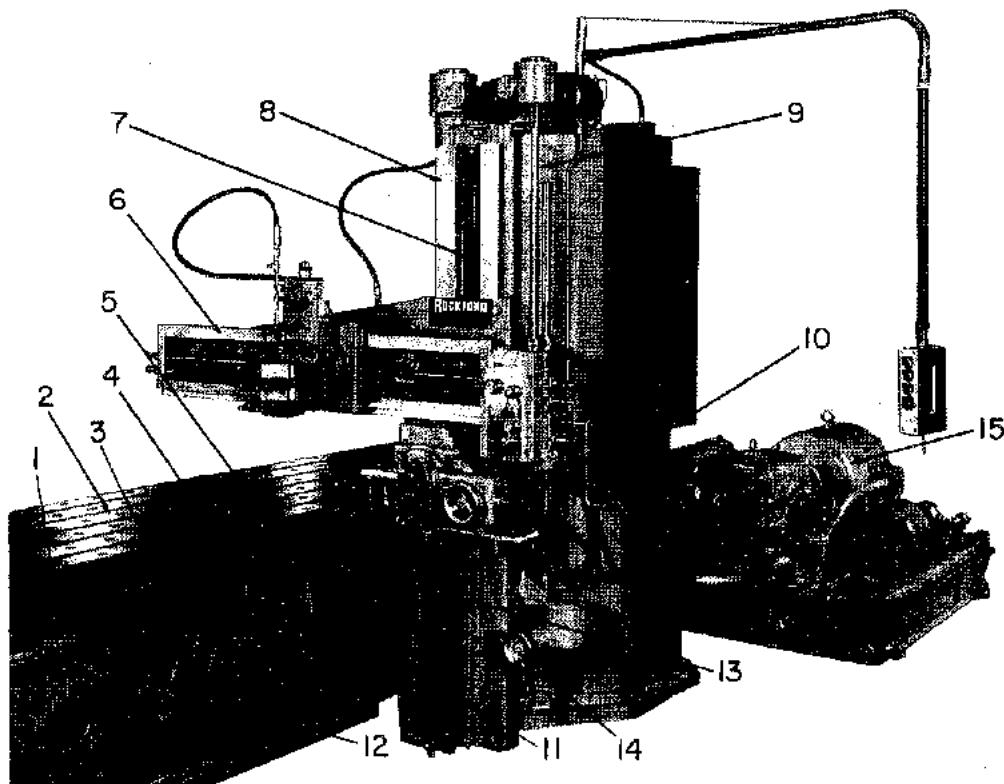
Nomenclatura de la acepillardora hidráulica (Rockford Machine Tool Co.)
